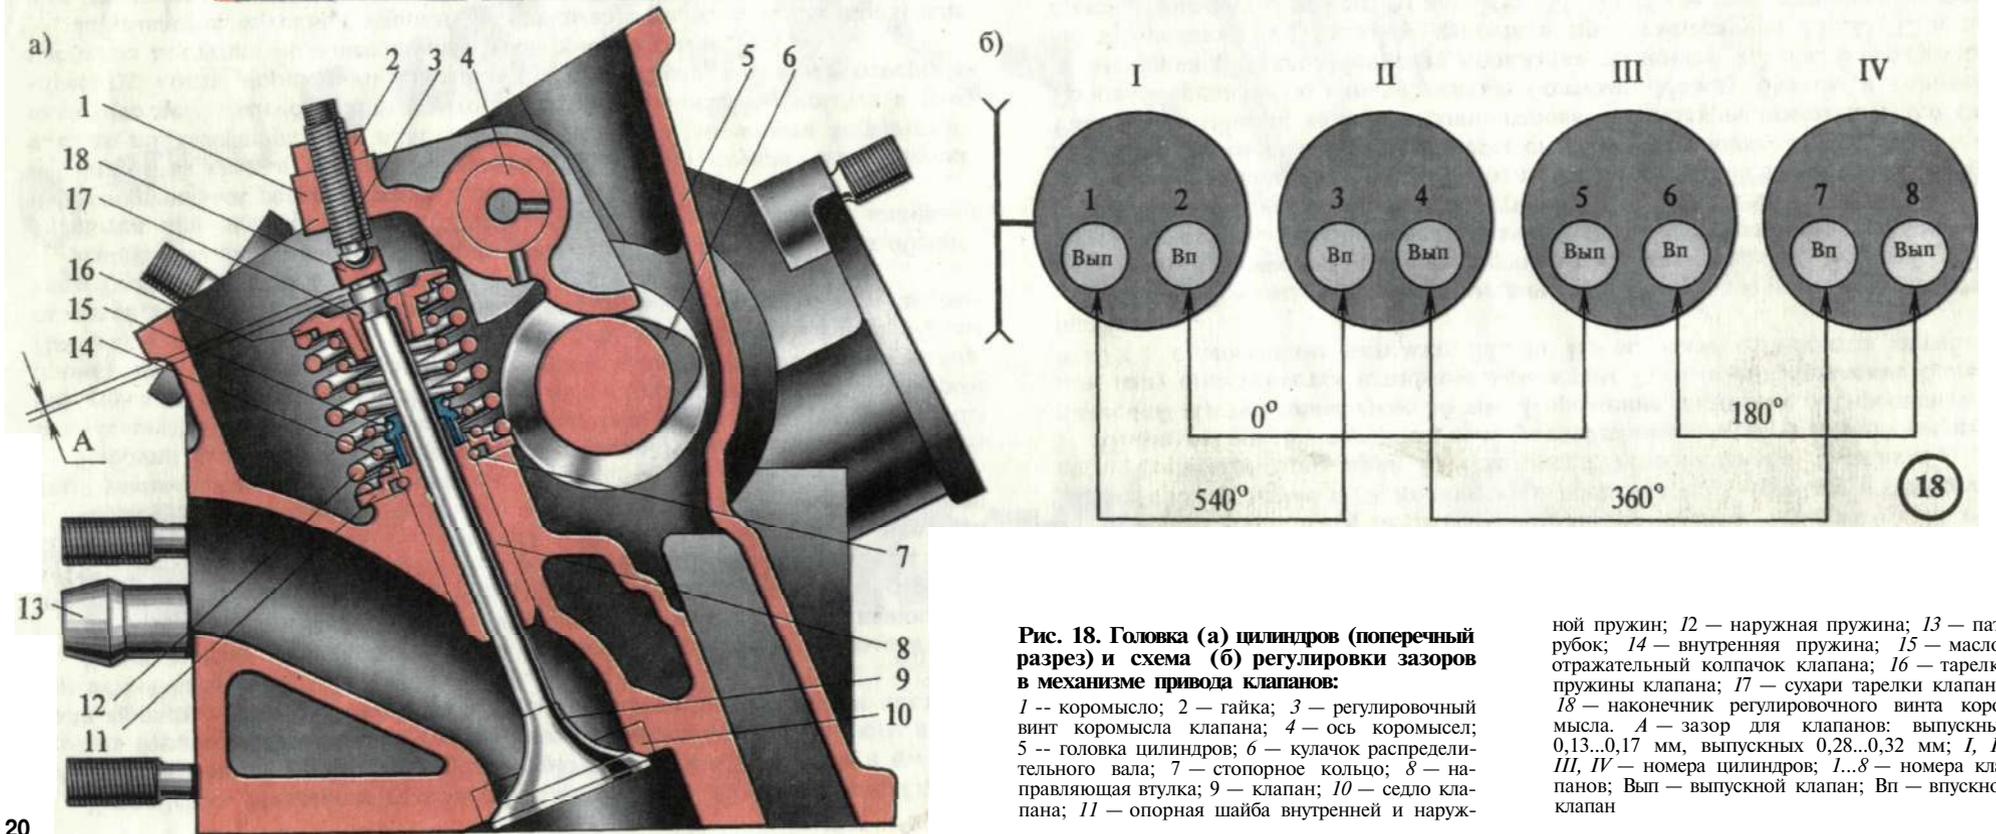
Головка (а) цилиндров (поперечный разрез) и схема (б) регулировки зазоров в механизме привода клапанов:
